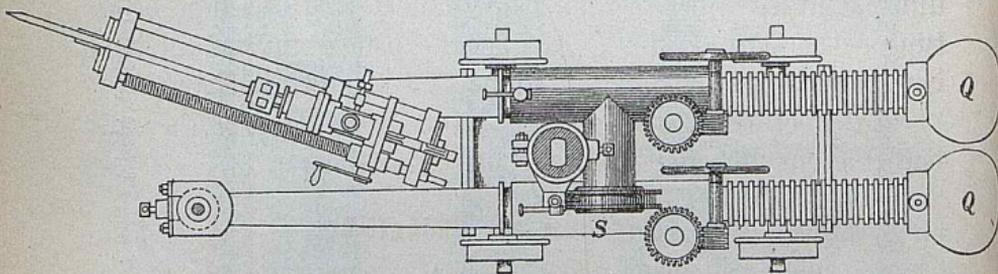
Humboldt'sches Gestell für Bohrmaschinen.
